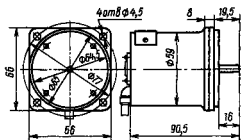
Габаритные и установочные размеры двигателей Г-31, Г-33, Г-34
